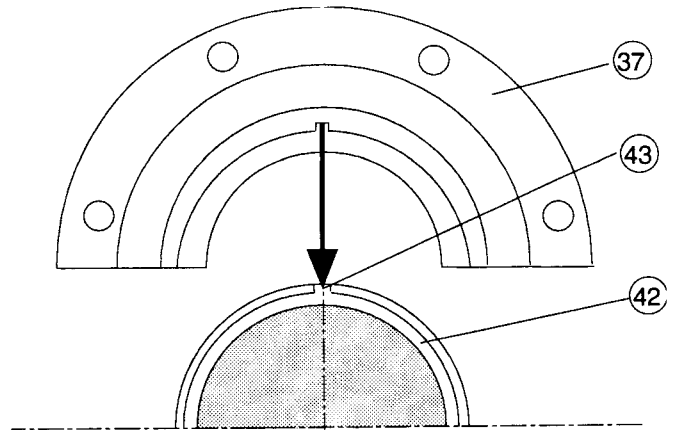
Установка держателя прокладки. Выровнять поверхности соединения держателя прокладки и картера.
